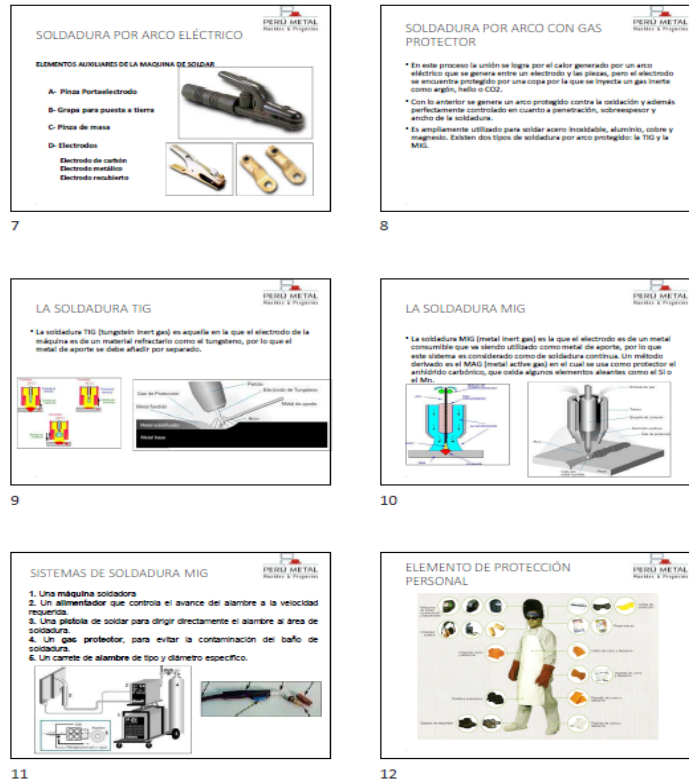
Láminas 7-12 de capacitación sobre técnicas de soldadura Fuente: Elaboración de los autores.
